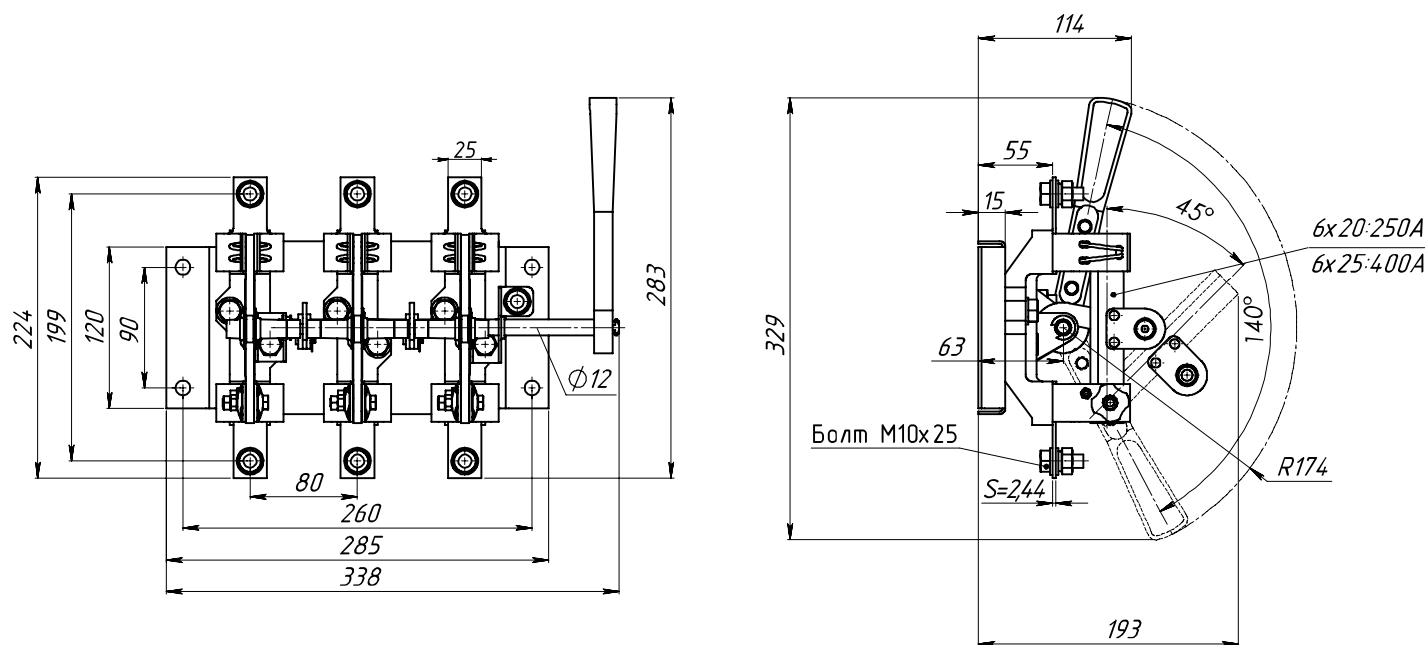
Разъединитель PE19-35(37)-31120-00 УХЛЗ с боковой рукояткой
